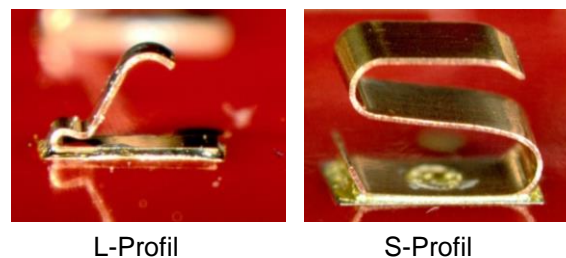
Auf einem PCB aufgebaute Federkontakte mit L- und S-Profil.
